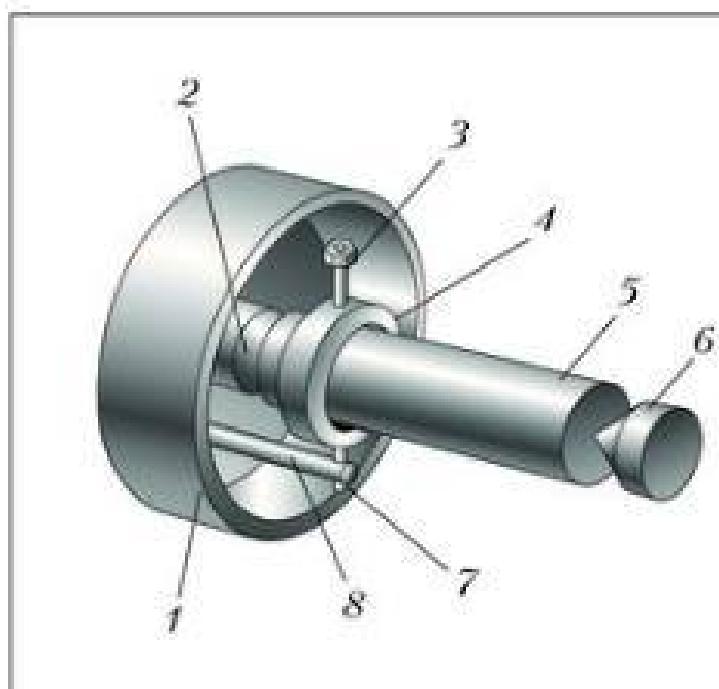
Установка заготовки с помощью поводковой планшайбы: 1 – корпус планшайбы; 2 – передний центр; 3 – стопорный винт; 4 – хомутик; 5 – заготовка; 6 – задний центр; 7 – стержень; 8 – поводок
